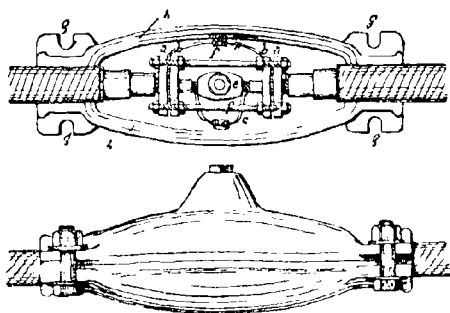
Boîte de jonction pour câbles concentriques (coupe et élévation extérieure).
